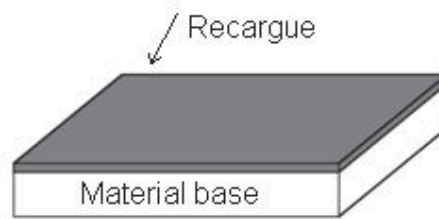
Recargue o recubrimiento por soldadura.
